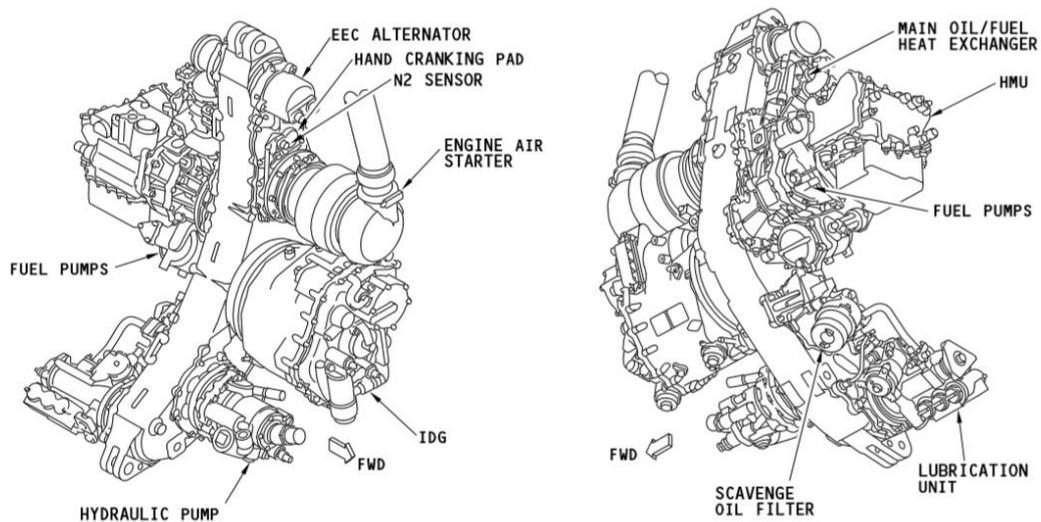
Componentes do accessory drive. Fonte: (AMM Chapter 72-00-00).
